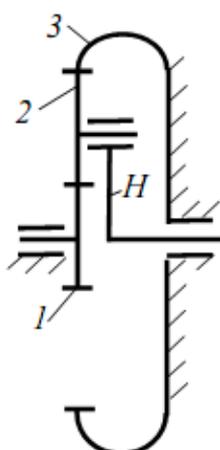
Кинематическая схема планетарного механизма Джеймса
